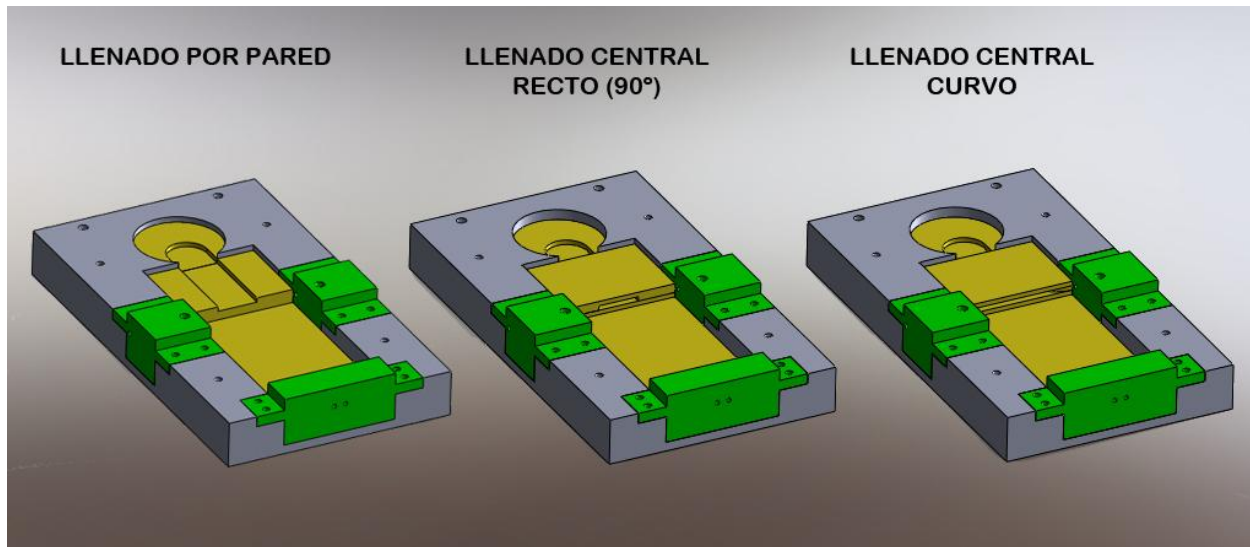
Configuraciones de llenado con espesor de 12 mm del molde de metacrilato.
